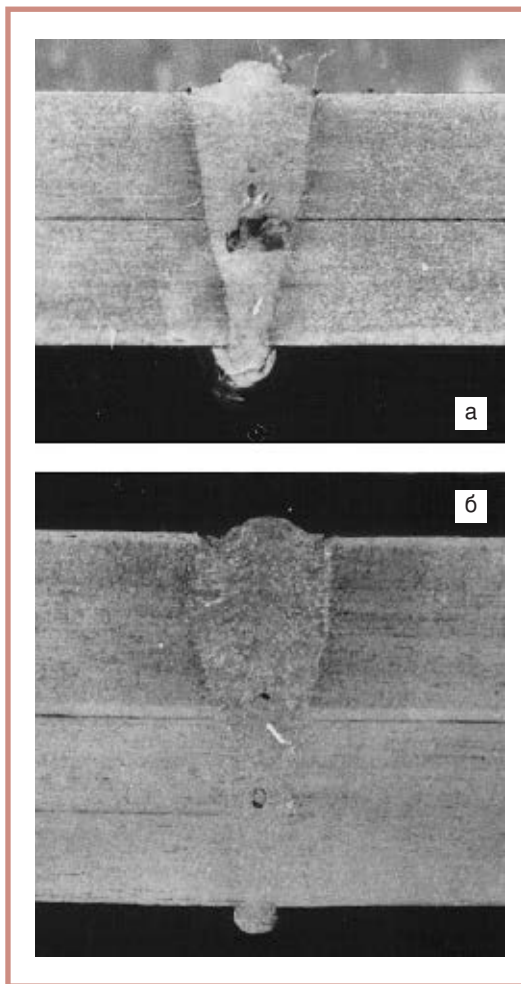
Поперечное сечение прорезного шва, выполненного лазерной сваркой (сталь Ст3кп): а — толщина листа 3 мм; б — толщина листа 5 мм
